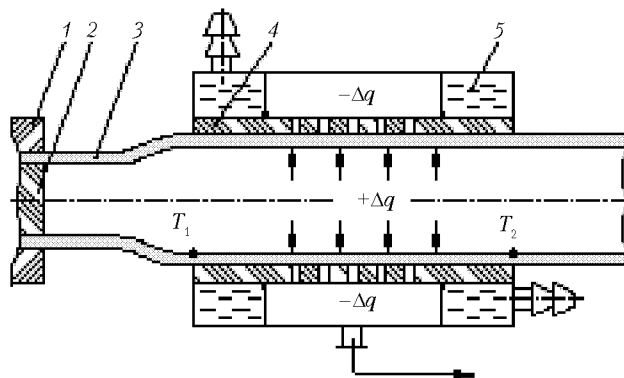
Схема вакуум-калибровки трубы: 1 – труба; 2 – дорн; 3 – изделие; 4 – калибрующая втулка; 5 – полости охлаждения
